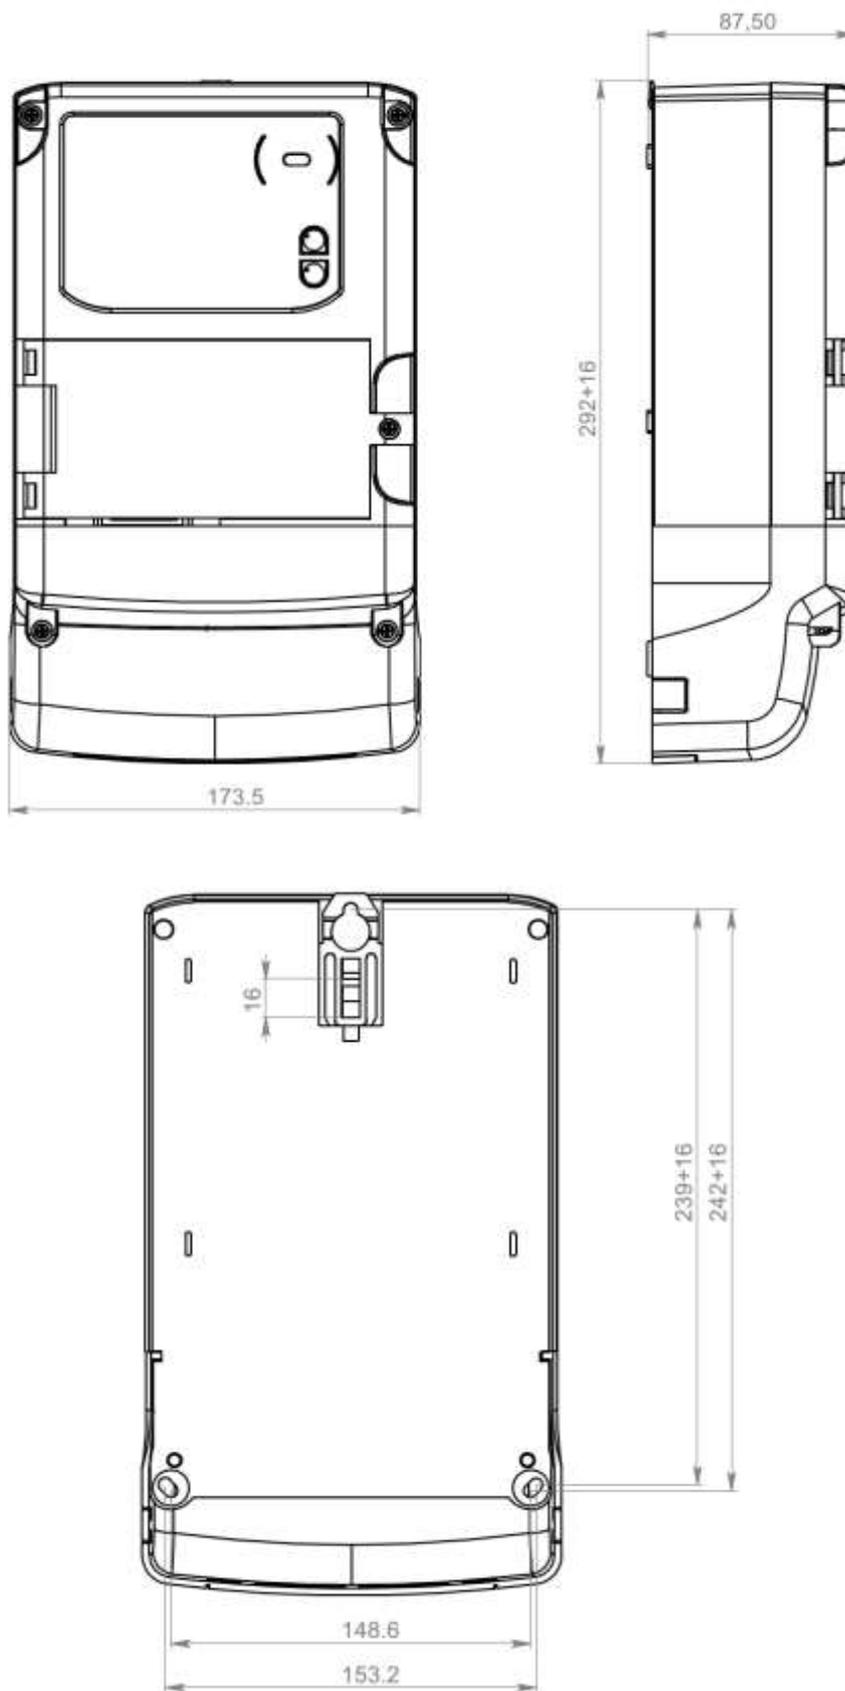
Габаритные и установочные размеры корпуса W32
